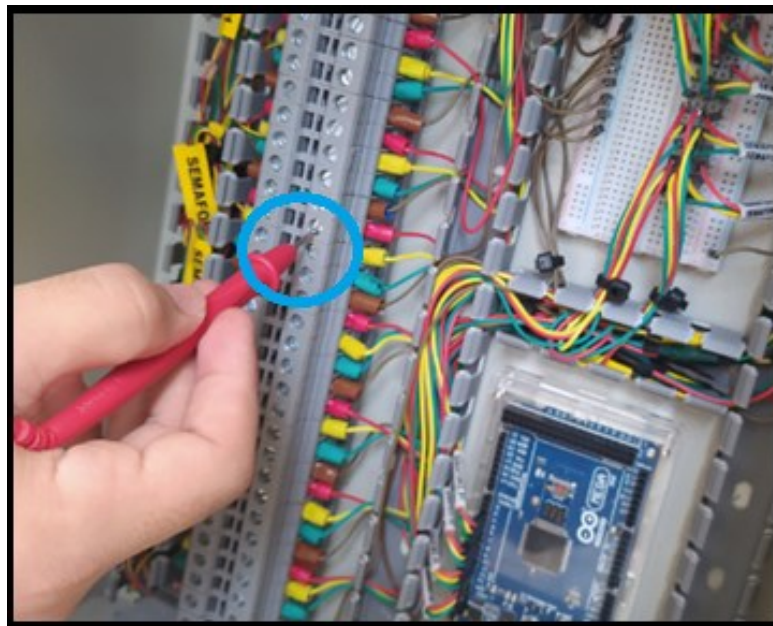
Revisión del estado de prensado de los cables en las bornas de conexión.
